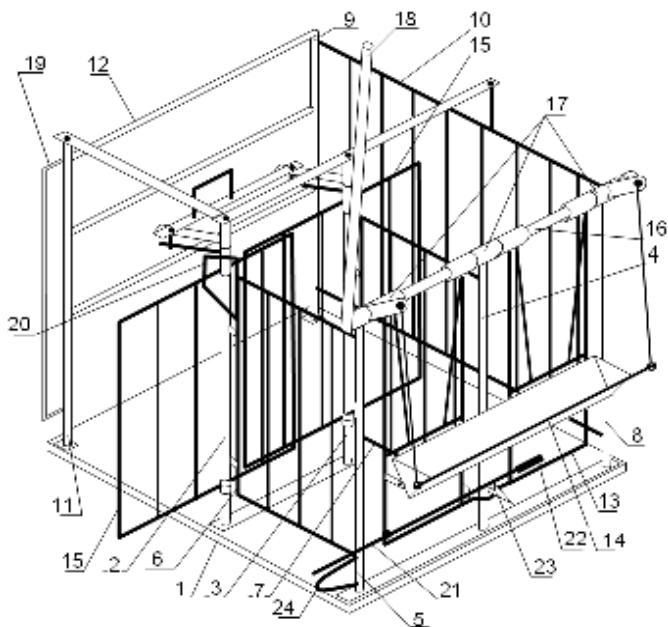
Конструкційно-технологічна схема двохстанкової установки лінійного типу для доїння овець
